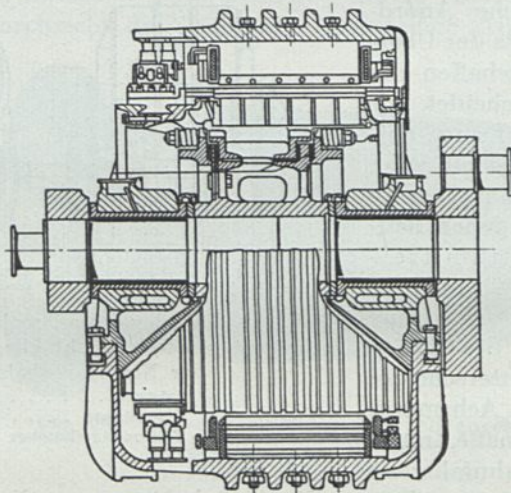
Längsschnitt durch den Motor der Lokomotive Abb. 242 (Rutschkupplung).
